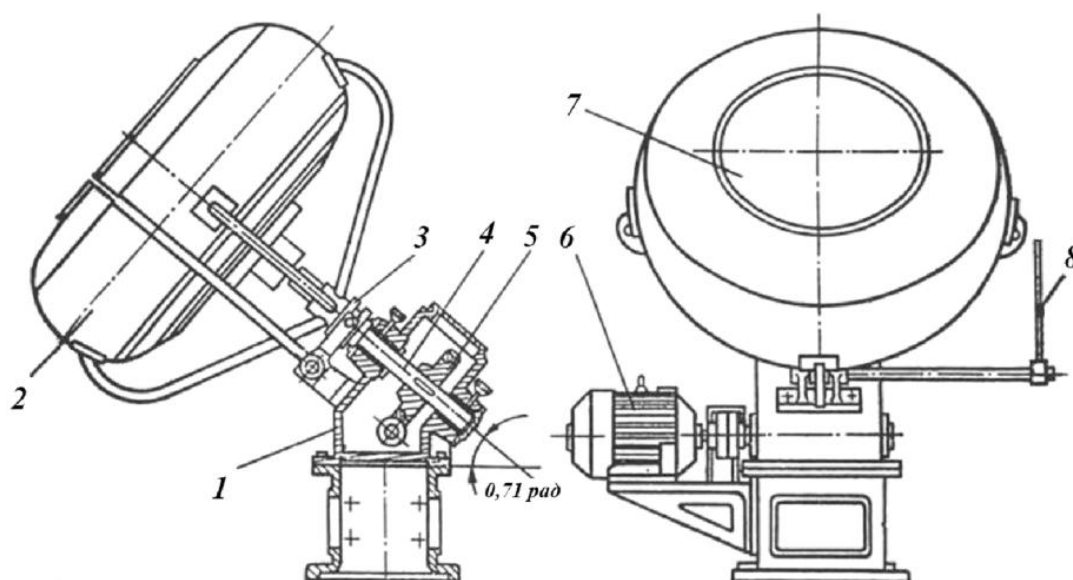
Дражировочная установка с гладкой внутренней поверхностью рабочего барабана:
